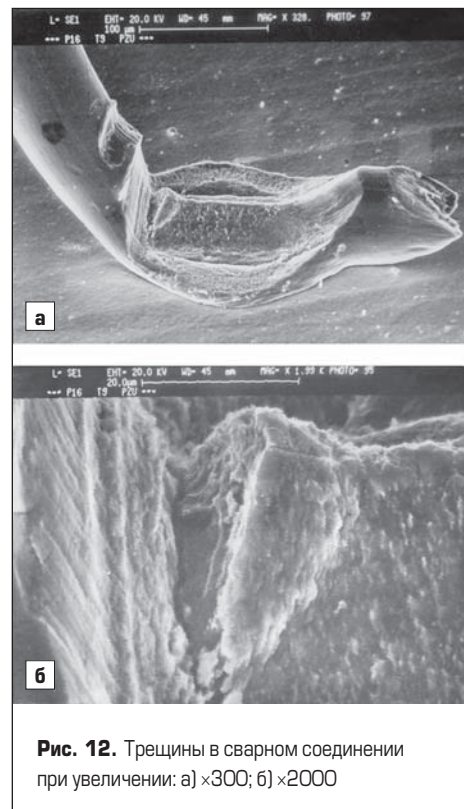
Трещины в сварном соединении при увеличении: а) $\times 300$; б) $\times 2000$
